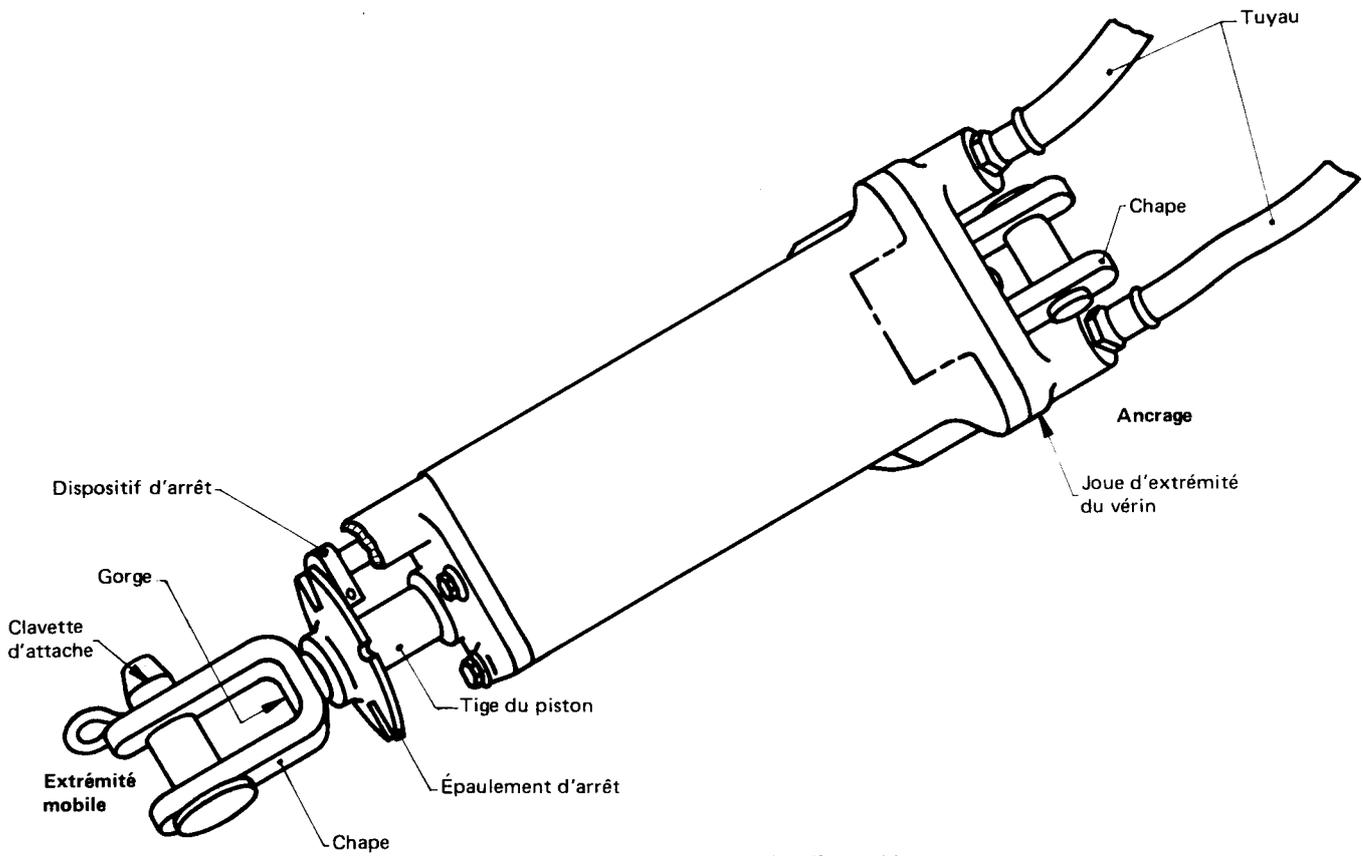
Vérin hydraulique – Vue d'ensemble
